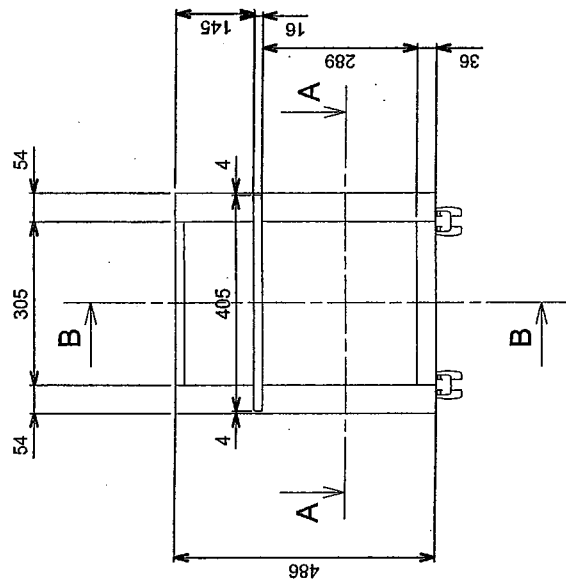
DETAIL ASSEMBLAGE PANNEAU FACE TIROIR
